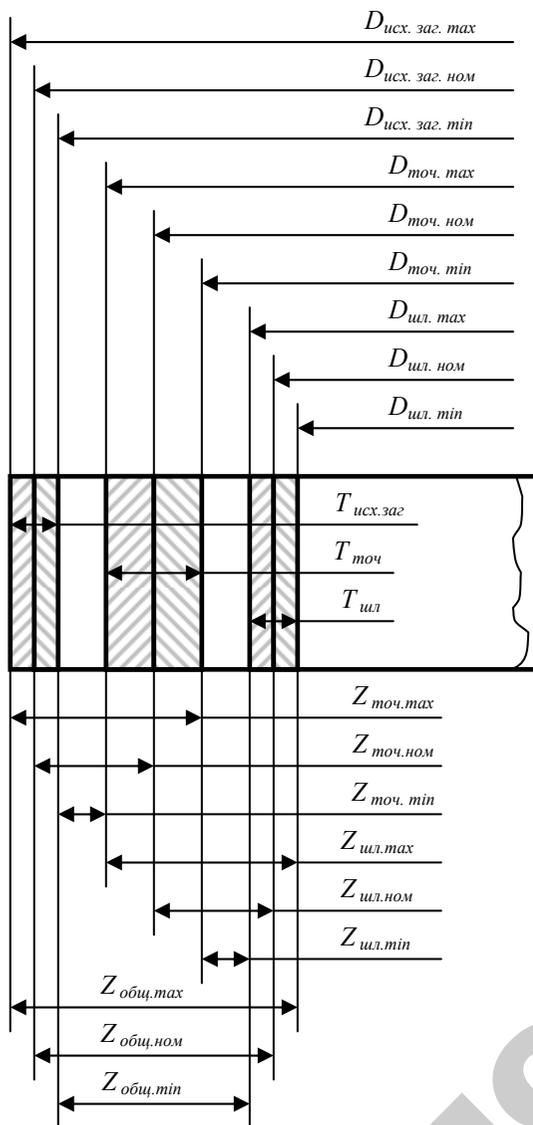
Схема расположения припусков и допусков на обработку заготовки вала точением и шлифованием
